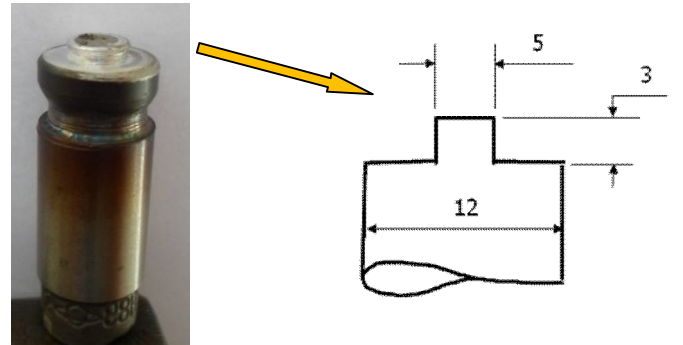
représentation de l'outil de soudage FSSW
